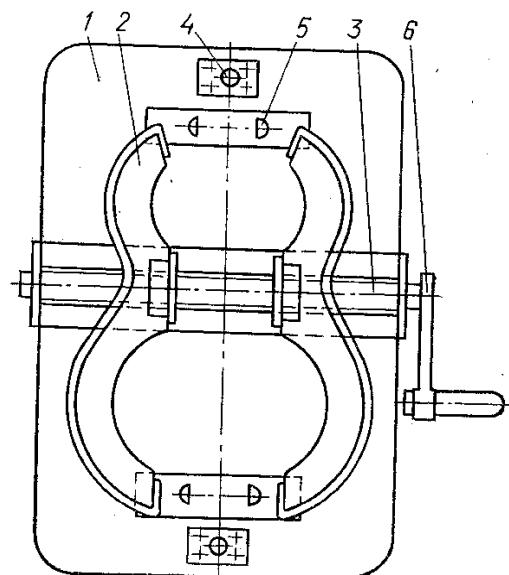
Разжимное приспособление для сборки рамки гитарного корпуса:
